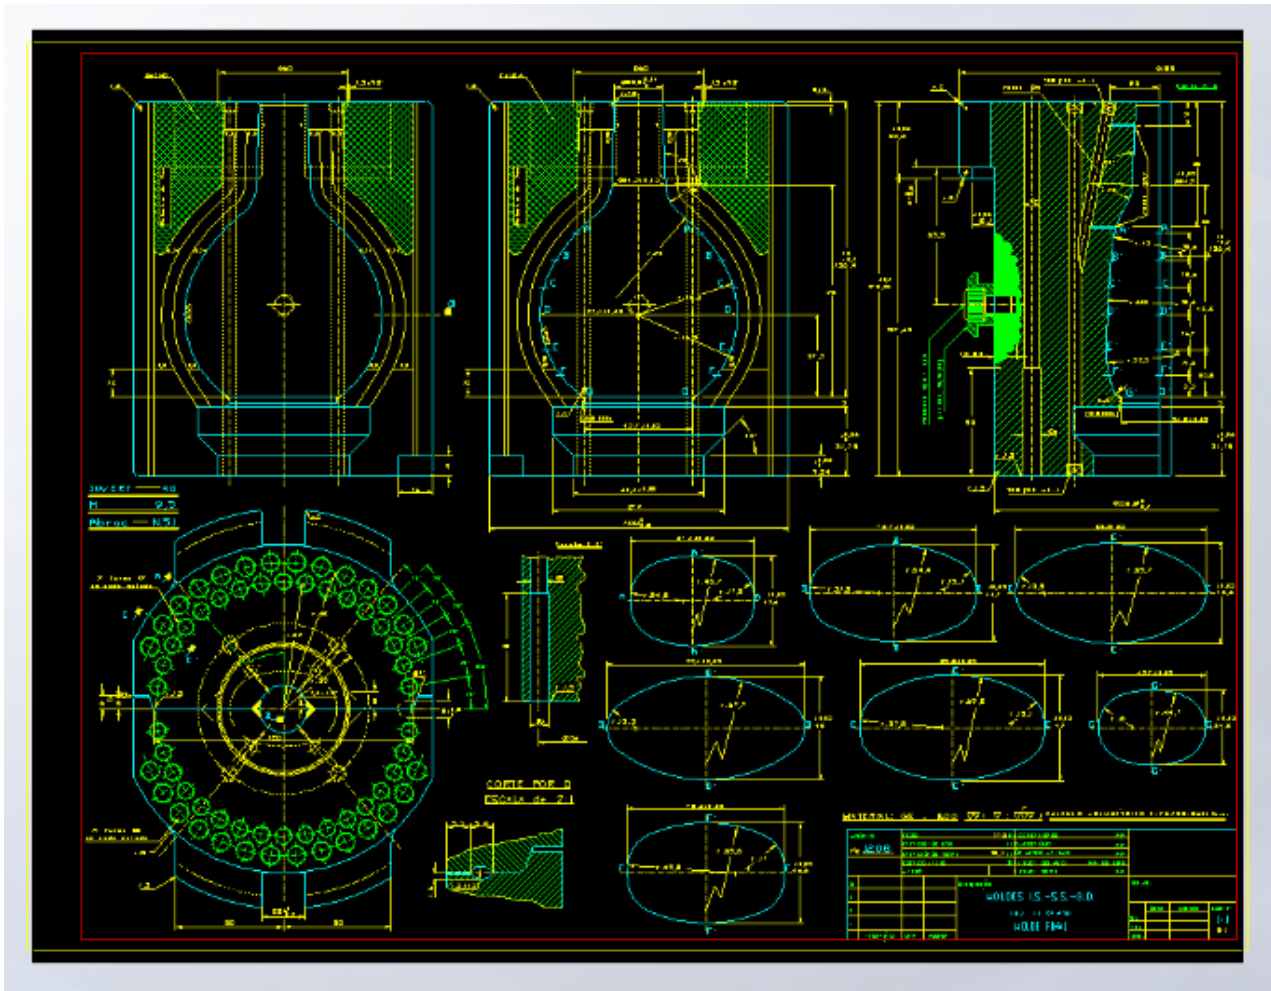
Desenho técnico do molde de acabar do cantil de Mateus Rosé 33cl.
